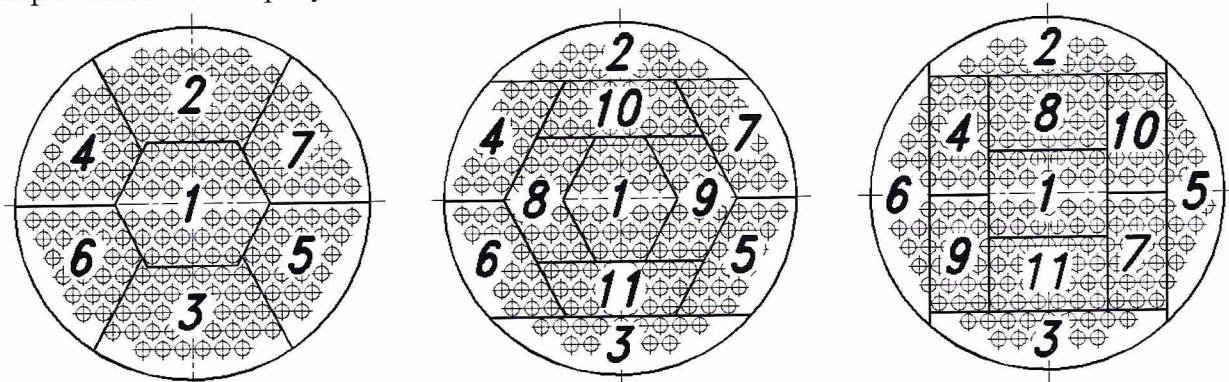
Примерные схемы деления трубной решетки на участки под сварку
